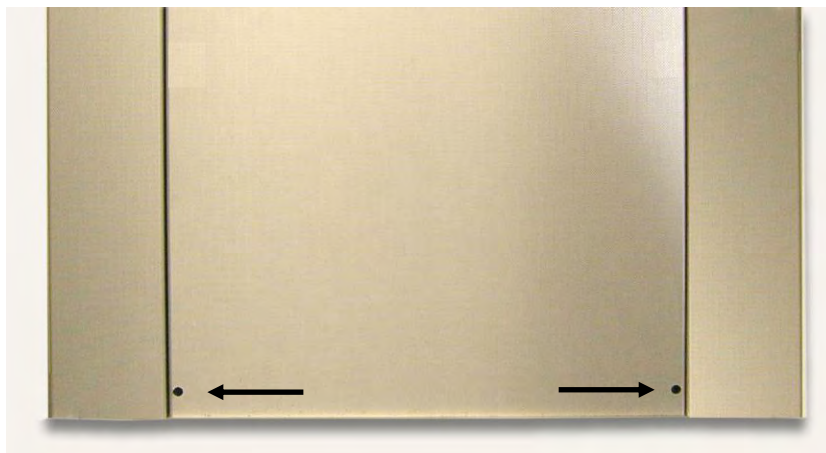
Position der 2 Zylinderschrauben mit Innensechskant
